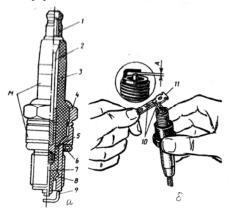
Свеча зажигания и регулировка зазора между электродами δ : A — зазор; M — место маркировки свечи; I — контактная гайка; 2 — контактная головка; 3 — изолятор; 4 — корпус; 5 — стеклогерметик; 6 — уплотнительное кольцо; 7 — центральный электрод; 8 — теплоотводящая шайба; 9 — боковой электрод; 10 — проволочные щупы; 11 — ключ для подгибания бокового электрода
